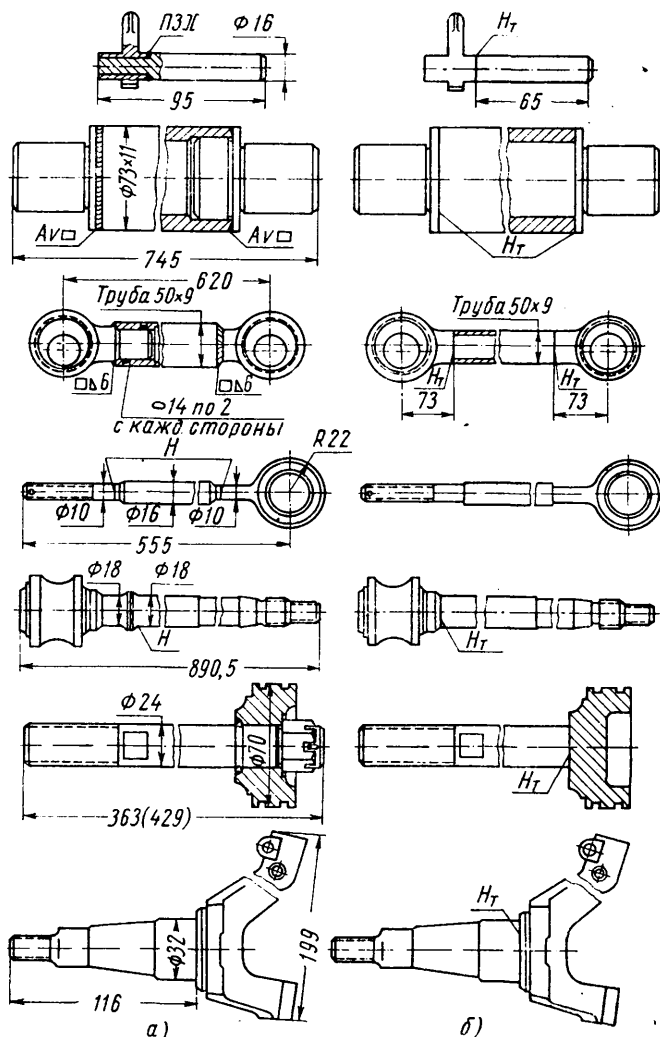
Конструкция деталей автомобилей «Урал» и «Москвич», предлагаемых для сварки трением:
